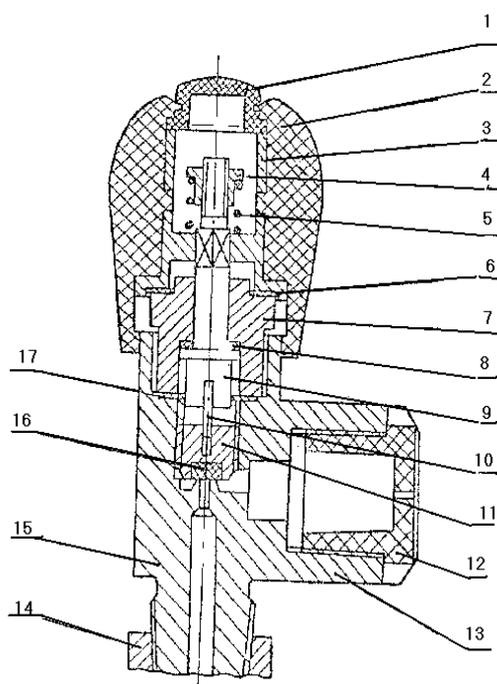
Вентиль: 1 – заглушка; 2 – облицовка; 3 – обойма; 4 – гайка; 5 – пружина; 6, 8, 17 – прокладка; 7 – сальниковая гайка; 9 – шточок; 10 – перо; 11 – клапан; 12 – заглушка; 13 – корпус; 14 – штуцер; 15 – вентиль; 16 – вставка
